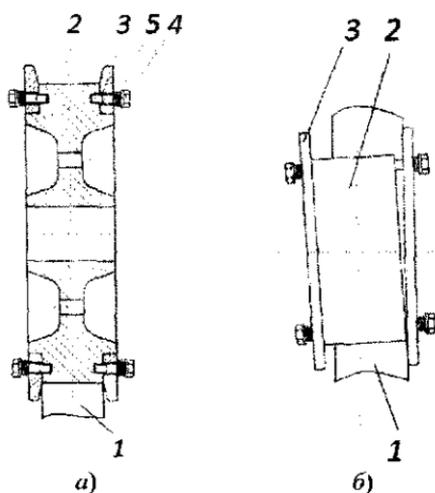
Крановое колесо: а – разрез; б – вид сверху.
